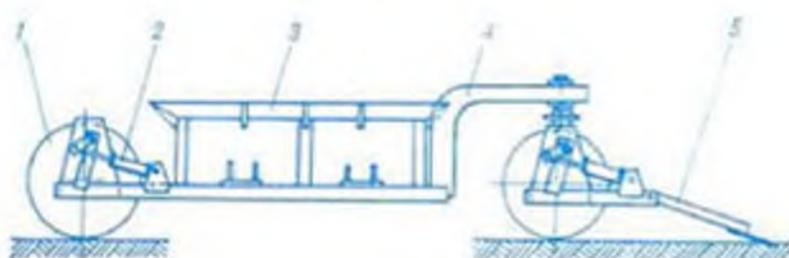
Прицепы. Прицеп-самосвал с опускающимся кузовом: 1 — ходовые колёса; 2 — механизм подъёма и опускания кузова; 3 — кузов; 4 — рама; 5 — дышло.
